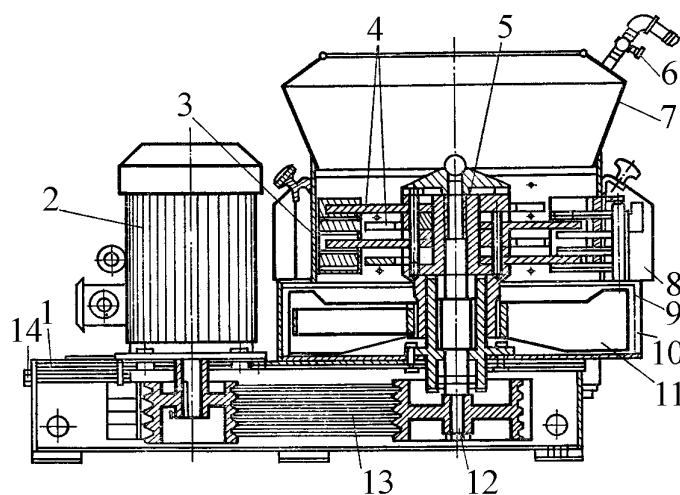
Общий вид измельчителя-смесителя кормов ИСК-3А:
